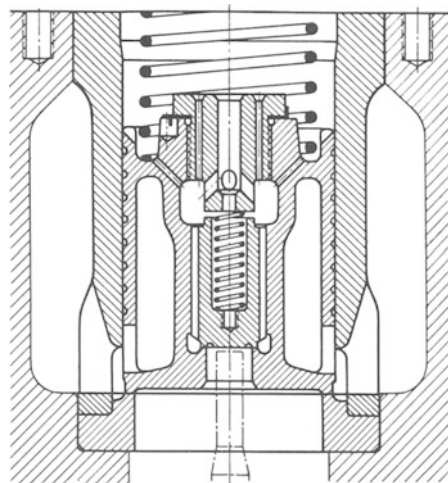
Einsitziges Dampfventil mit eingebautem Entlastungsventil.
